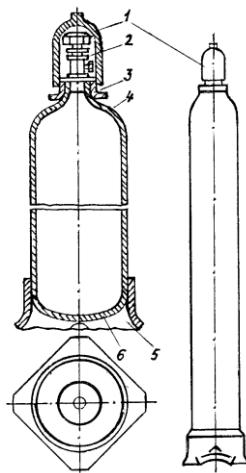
Схема газового баллона: 1 – защитный колпак; 2 – запорный вентиль; 3 – кольцо с резьбой для навертывания защитного колпака; 4 – горловина; 5 – башмак; 6 – сферическое днище
